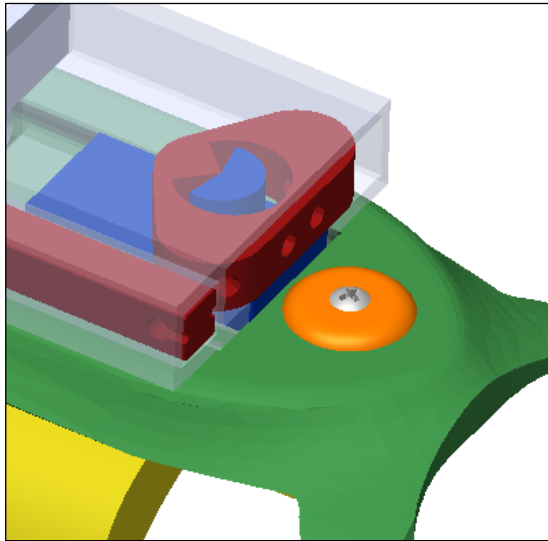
Nueva unión entre las piezas Rotating Gauntlet y Fixed Gauntlet
